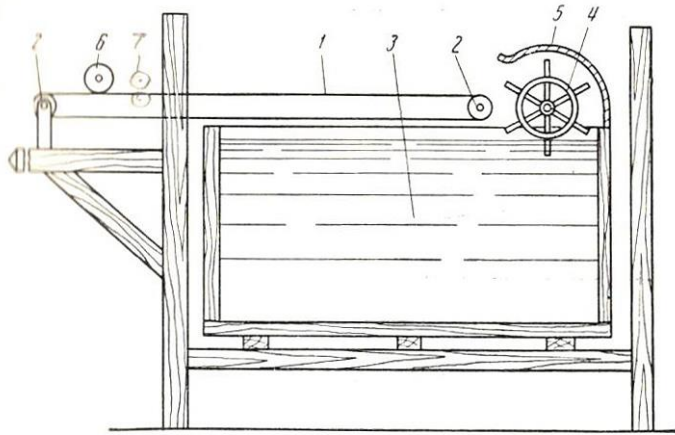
«Самочерпка» Робера: 1 – сетка; 2 – натяжные валики; 3 – черпальный чан; 4 – черпальное колесо; 5 – отражательный щиток; 6 – пресс; 7 – накат
